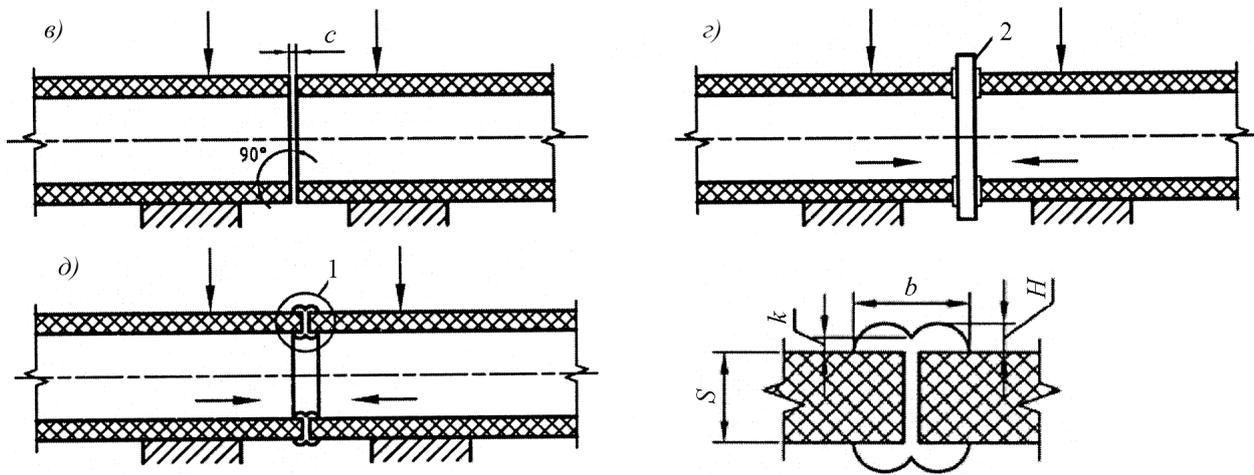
, лист 1 – Последовательность процесса сборки и сварки труб нагретым инструментом
